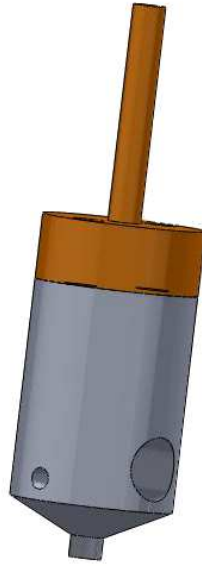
Herramienta diseñada tras ensamblar ambas piezas.
